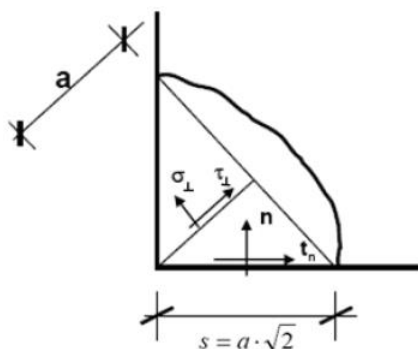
Tensiones abatidas en el cordón de soldadura.
